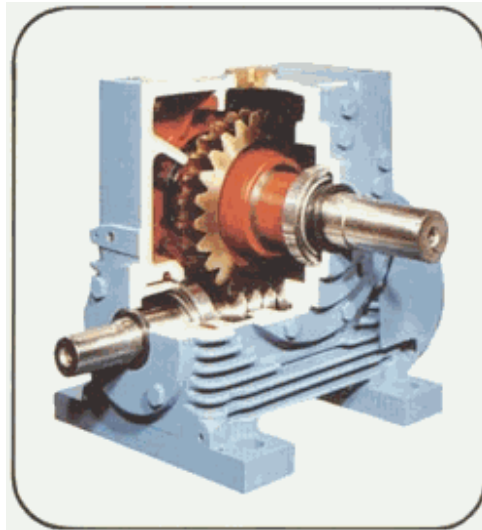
Aplicación de engranajes helicoidales tipo sin fin.
